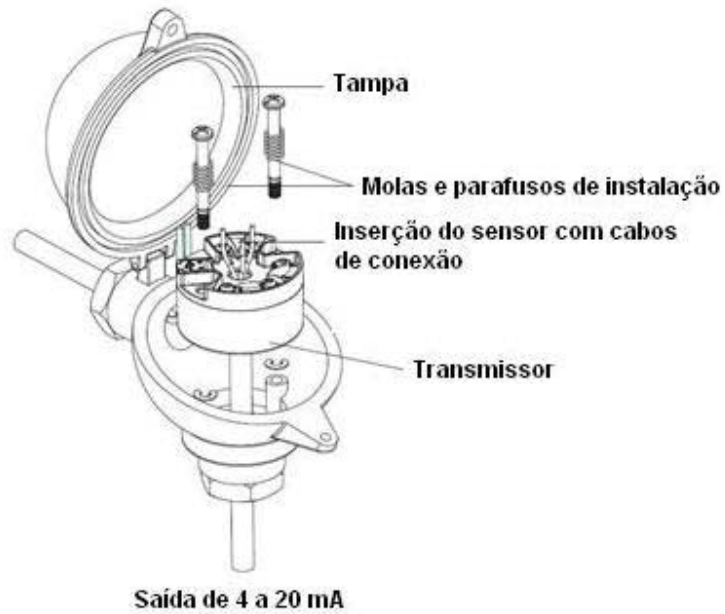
Instalação do transmissor MST110 num cabeçote Form B
